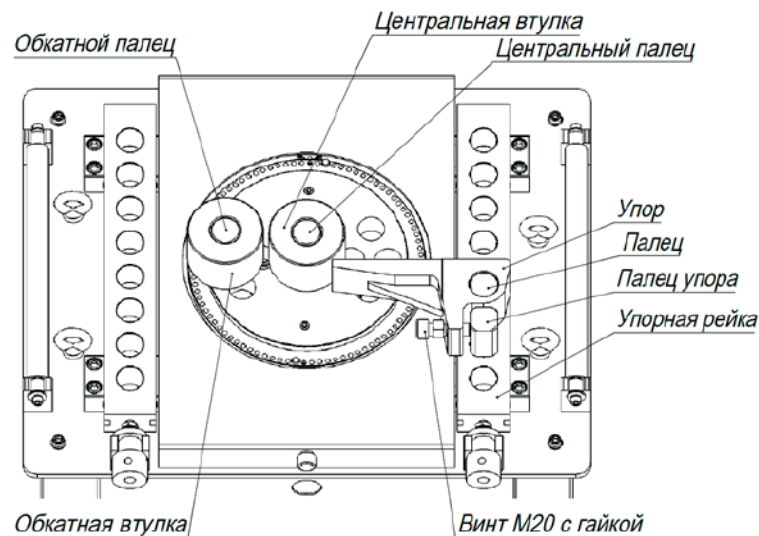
Схема расположения гибочных приспособлений (VPK Г-55)
